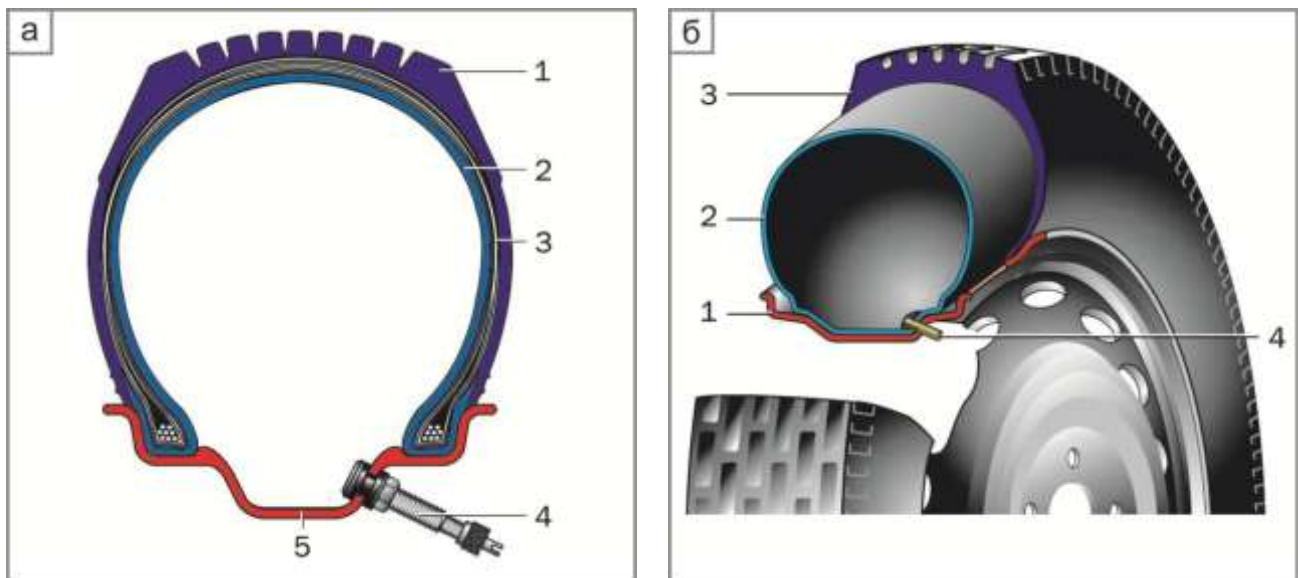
Конструкція колеса (а) з безкамерною шиною: 1 – протектор; 2 – герметизуючий повітронепроникний гумовий шар; 3 – каркас; 4 – вентиль колеса; 5 – обід; (б) з камерної шиною: 1 – обід колеса; 2 – камера; 3 – шина (покришка); 4 – вентиль
